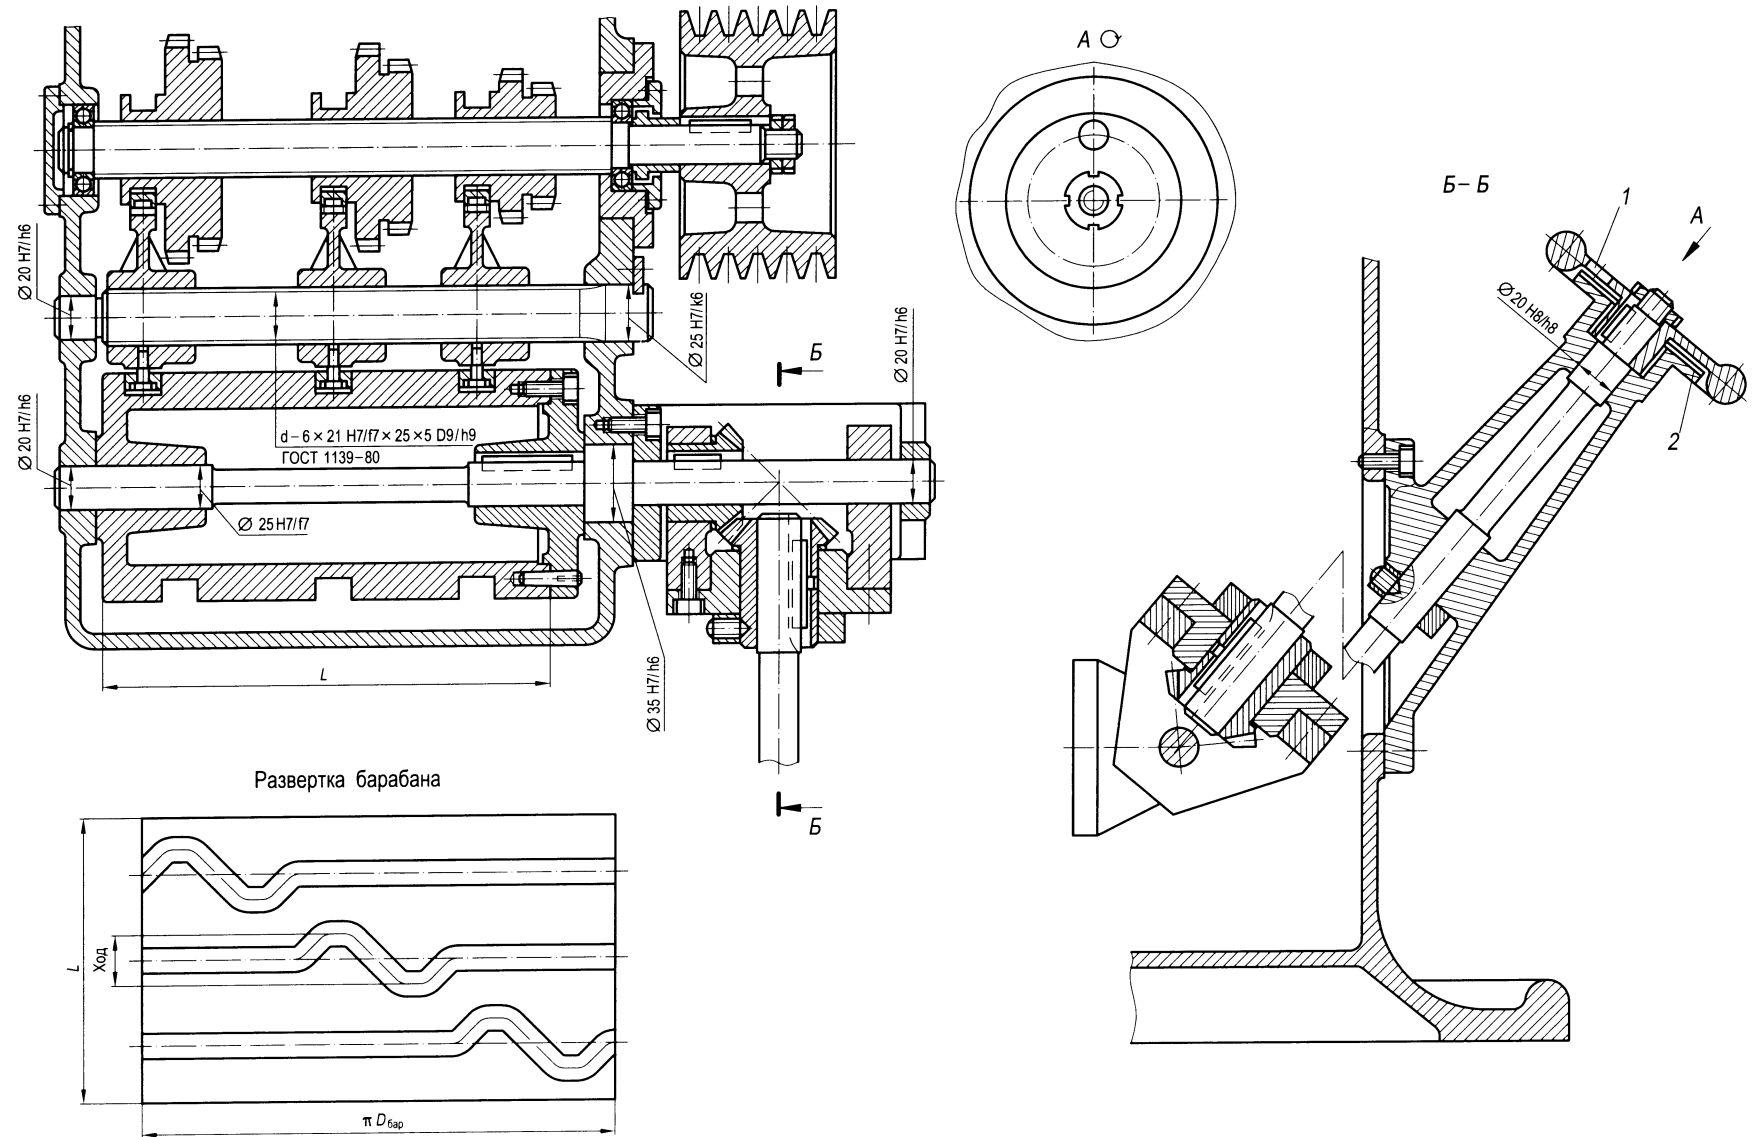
Механизм передвижения зубчатых колес барабанным кулачком:
